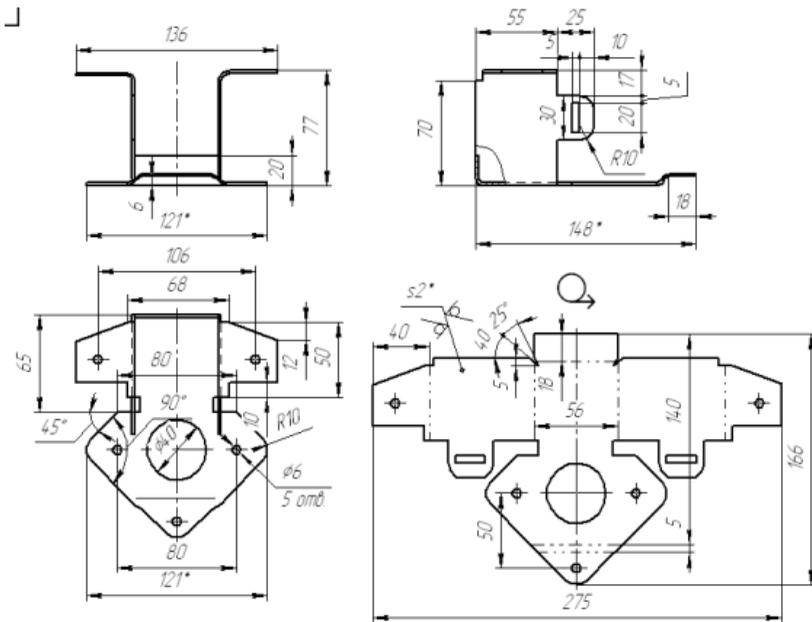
Оформление чертежа детали и развертки на одном листе
